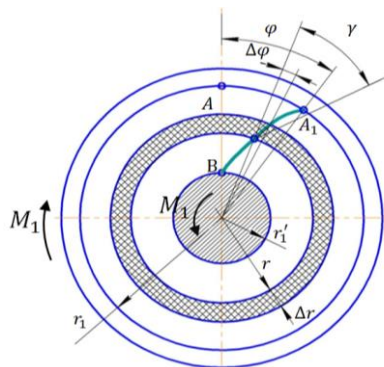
Схема для расчета деформации сдвига амортизатора-втулки шестерни зубчатой передачи
